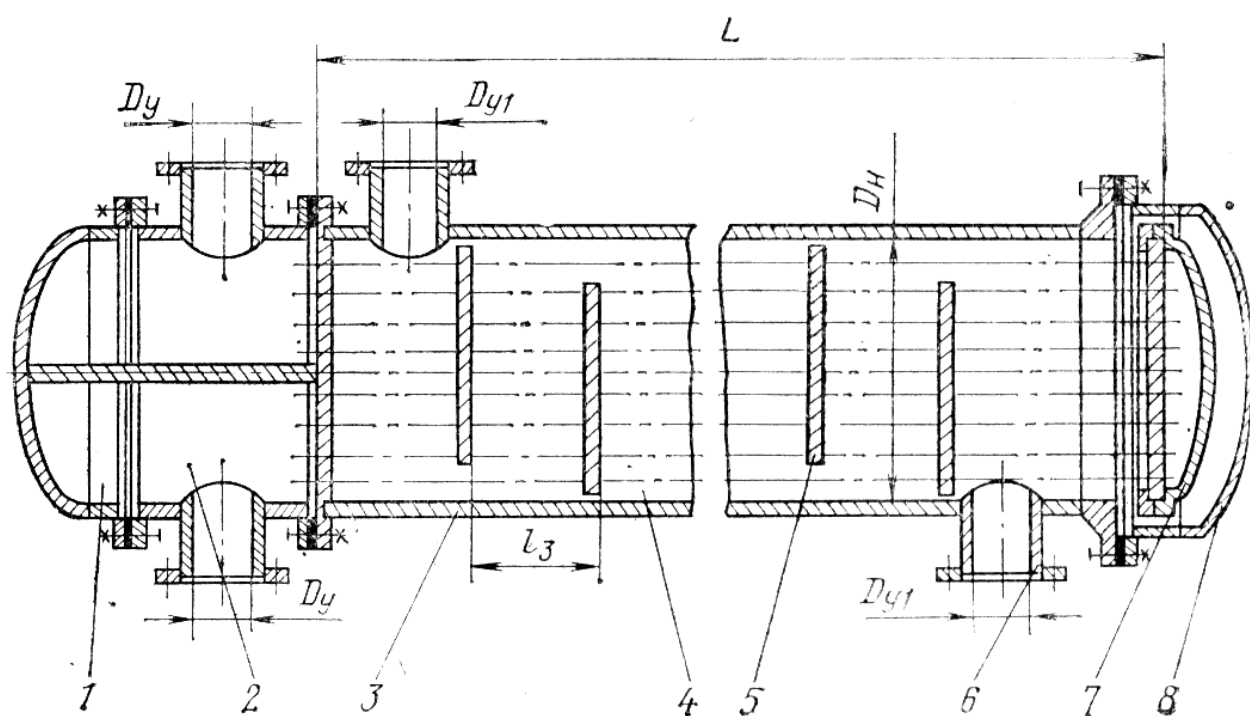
Кожухотрубчатый холодильник с плавающей головкой
